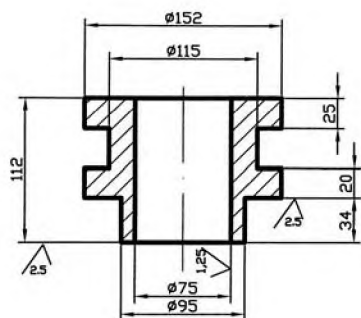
Эскиз детали «втулка опорная» из стали 40 массой 7,1 кг, изготовленной из прутка механической обработкой
